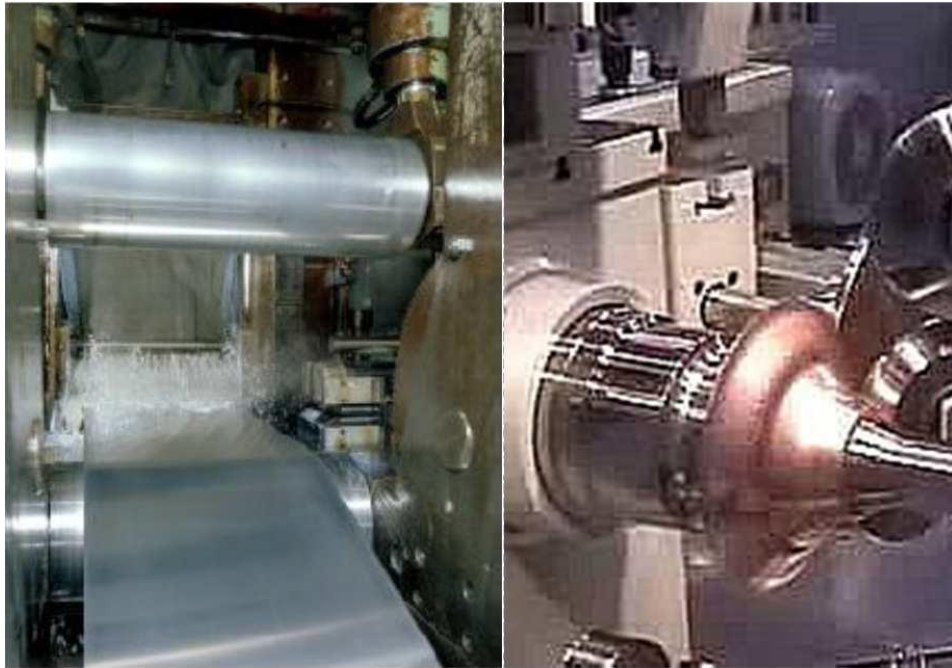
Laminación en frío (Izquierda) y conformado rotativo de chapa (derecha)
